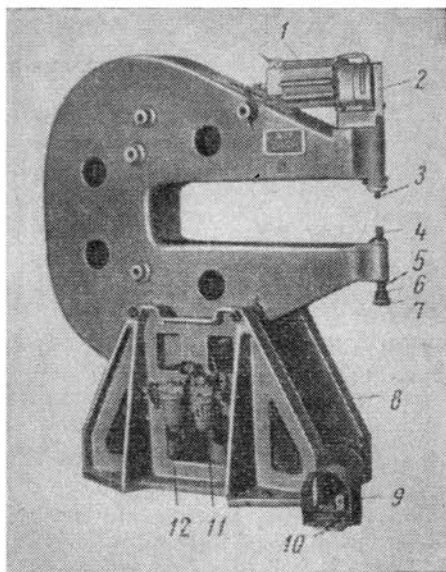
Пневморычажный стационарный пресс КП-204М для одиночной клепки
